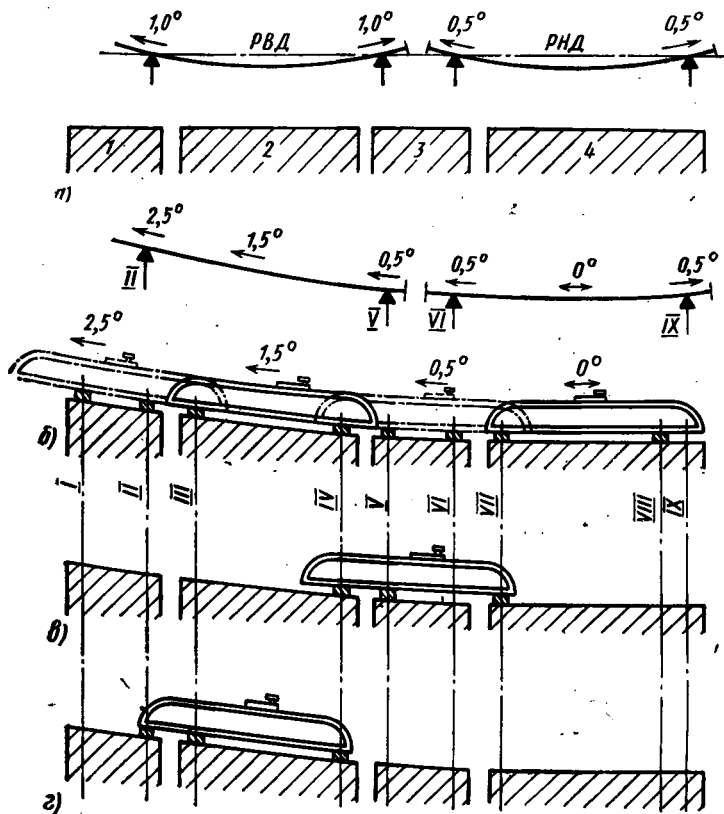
Схема центровки корпусов турбины и подшипников по уровню:
